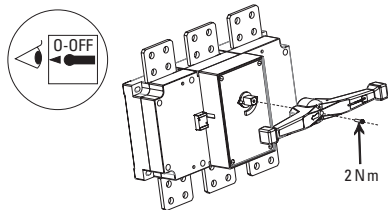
а – Монтаж ручки на корпус рубильников 1000-1600 А
